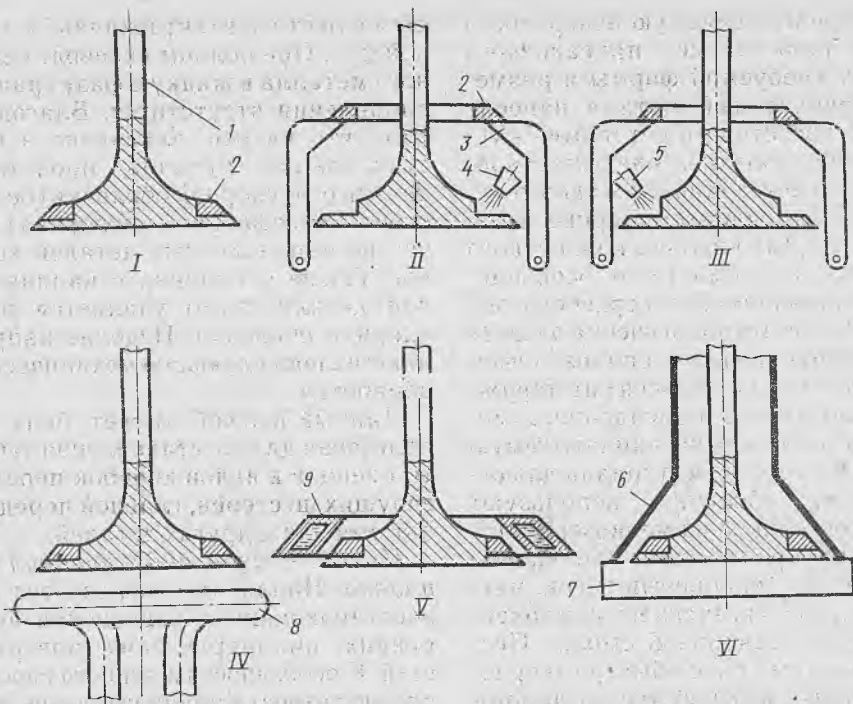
Схема наплавки клапанов монолитным присадочным материалом: 1 — деталь; 2 — кольцо присадочного сплава; 3 — защелки; 4 — сопло для подачи флюса; 5 — сопло для подачи масла; 6 — камера охлаждения; 7 — вращающийся кристаллизатор; 8 — индуктор для предварительного нагрева; 9 — основной подвижной индуктор
